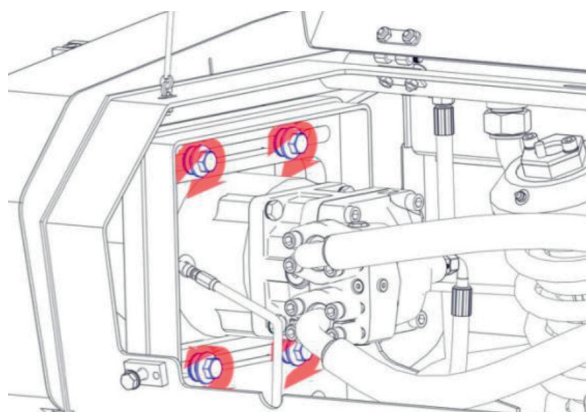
Замена ремня: ослабить регулировочный винт. Ослабьте регулировочный винт М16. Подшипник промежуточного вала свободно перемещаем.
